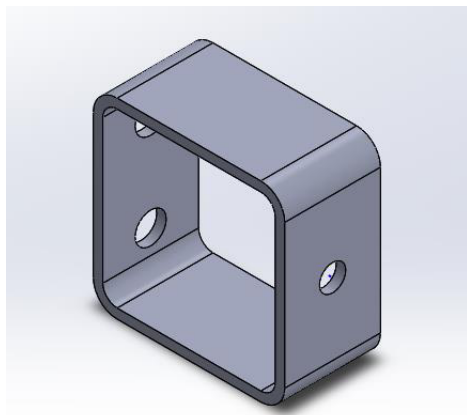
Cuadrado anclaje cable (SolidWorks).
